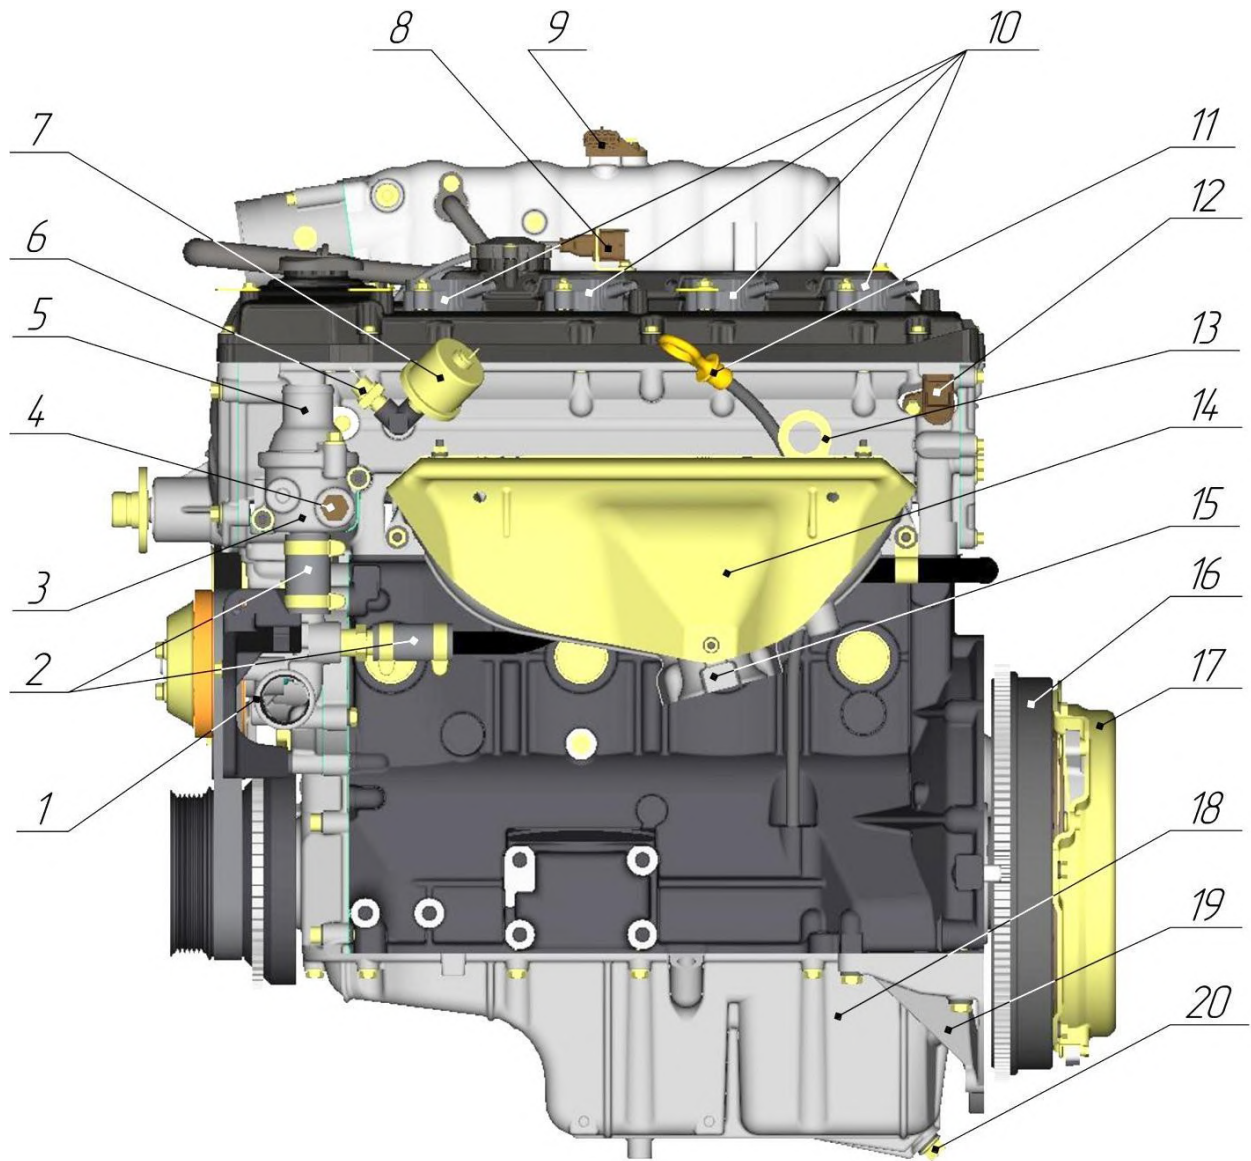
Ansicht des Motors ZMZ-40905.10 von rechts:
